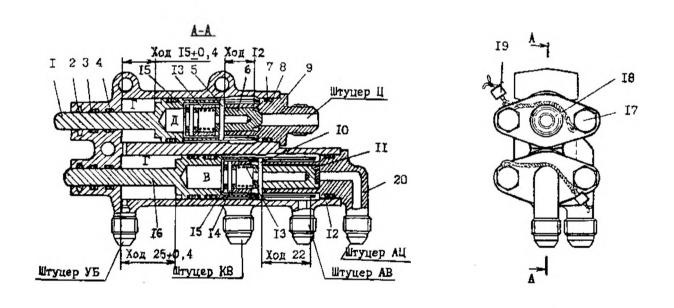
Блок цилиндров открытия замков убранного положения ГОШ 1,16 — шток; 2,4,7 — уплотнительное кольцо; 3,8 — защитная шайба; 5,10,14 — штифт; 6,11 — обратный клапан; 9,20 — крышка; 12 — корпус; 13 —пружина; 15 — втулка; 17 — болт; 18 — контровка; 19 — пломба
